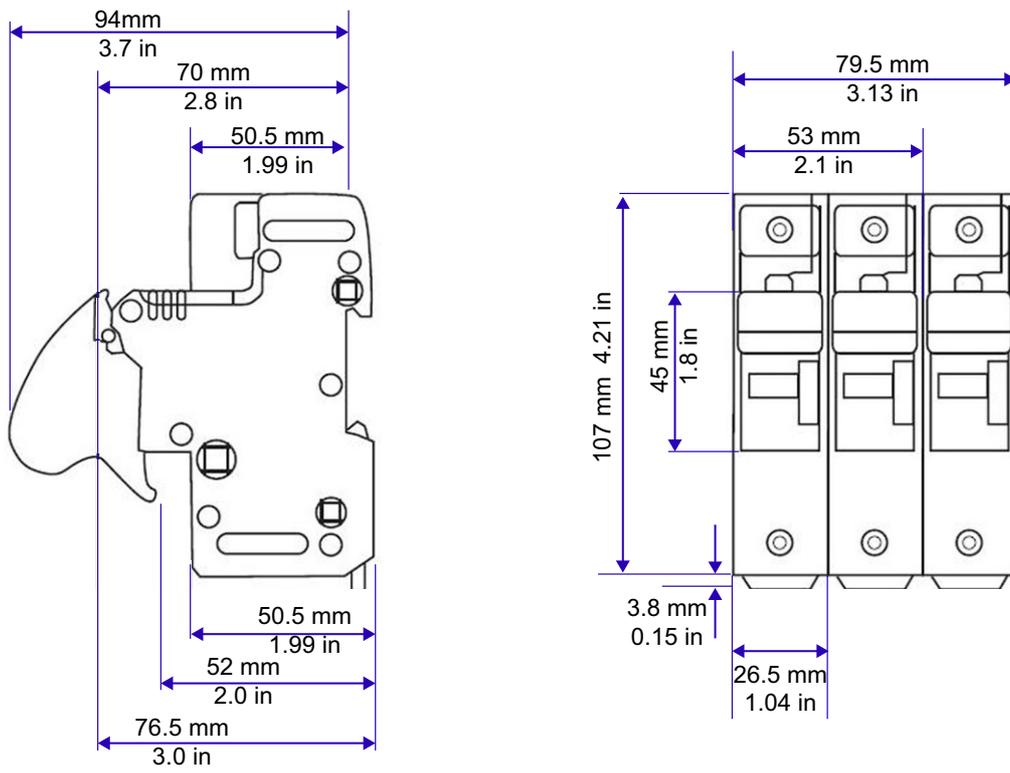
Dimensions des porte-fusibles : US143 (14x51 mm)
